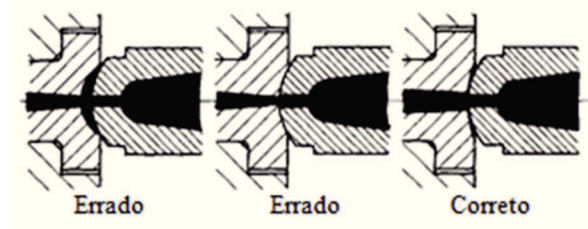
Montagem do injetor do molde e bico da máquina de injeção (Provenza, 1976).
